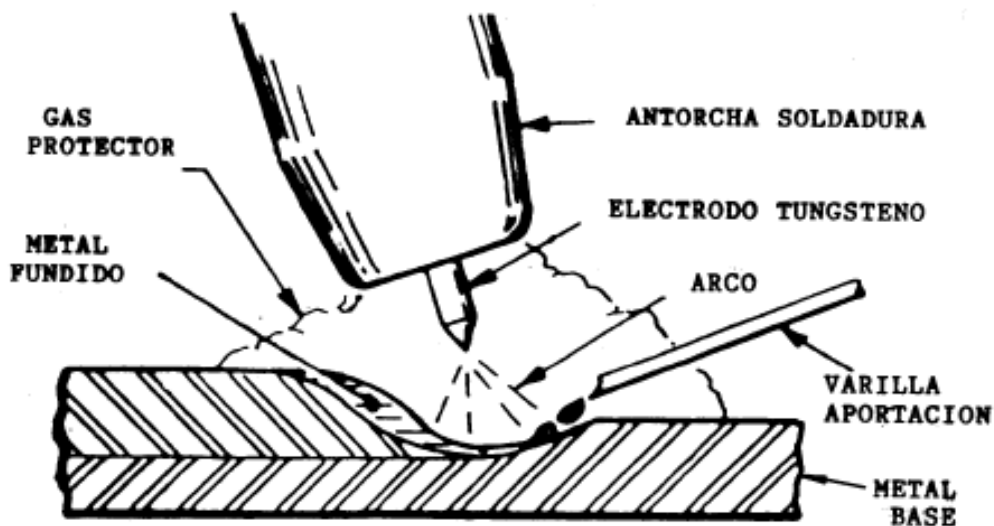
Elementos que intervienen en la soldadura TIG
